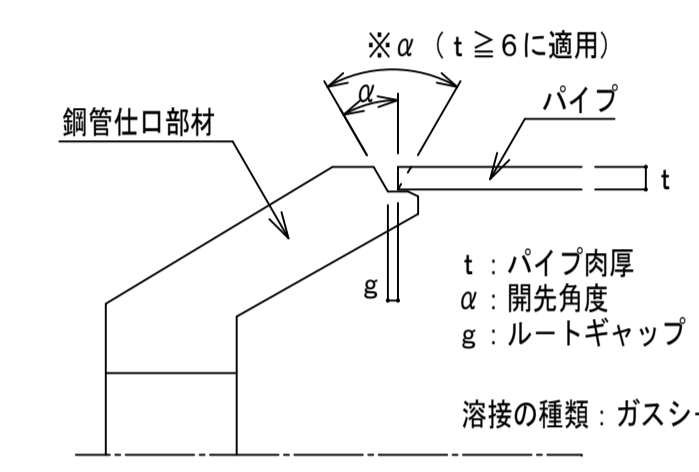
：パイプと鋼管仕口部材の溶接部開先形状図
